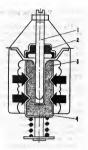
Восстановление термостата: 1 — порщень; 2 — резиновая вставка; 3 — наполнитель; 4 — корпус циляндра. Стрелками указаны места деформирования цилиндра для уменьщения его вичтоениего
